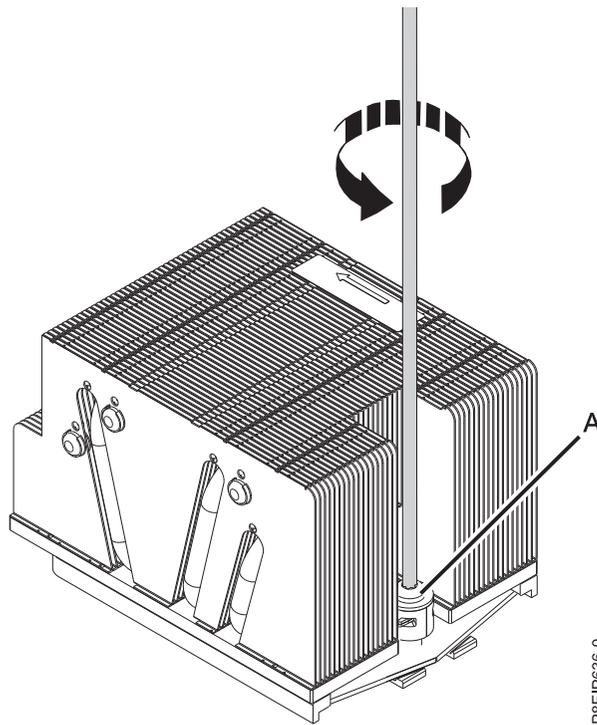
Desserrage de la vis du bras de chargement du dissipateur thermique
